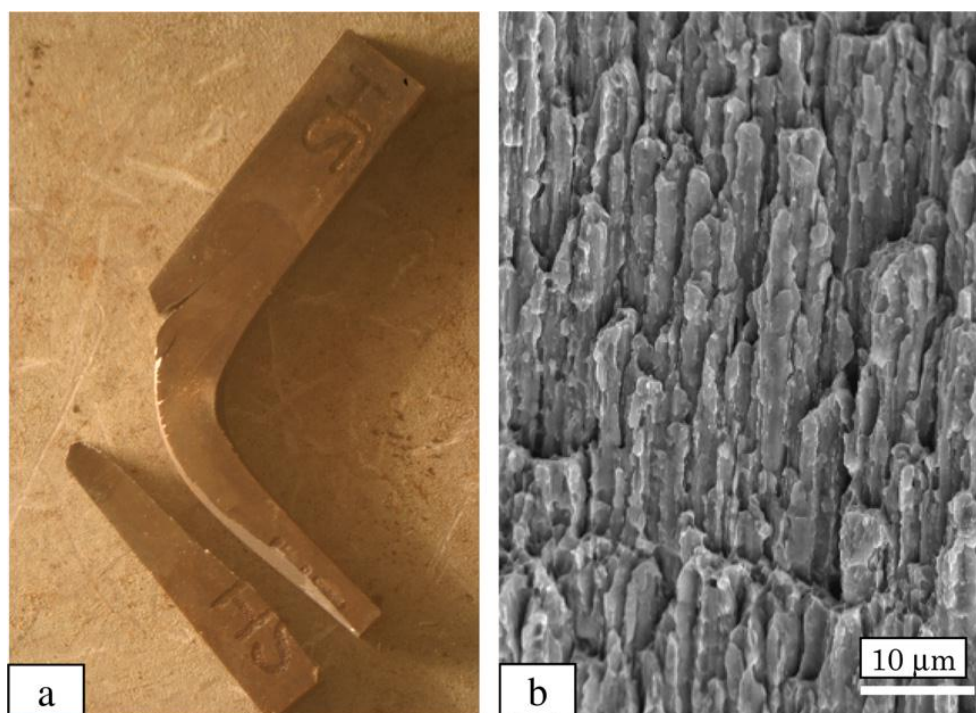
Vues a) macroscopique et b) microscopique d'une éprouvette Charpy issue de l'acier ODS MA957 irradié à 42 dpa à 325°C rompue par bifurcation [Henry-2011].
